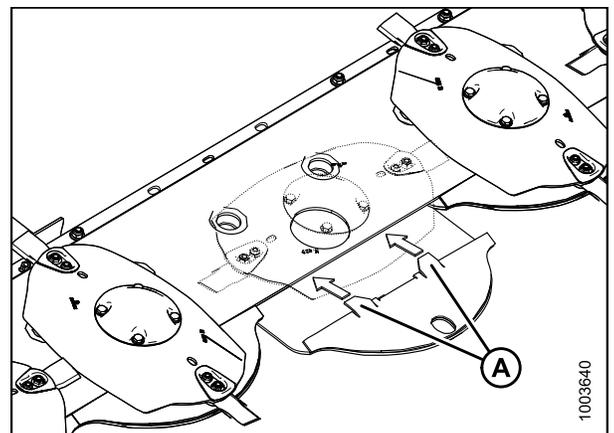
Jupe pare-pierres installée sur la barre de coupe
